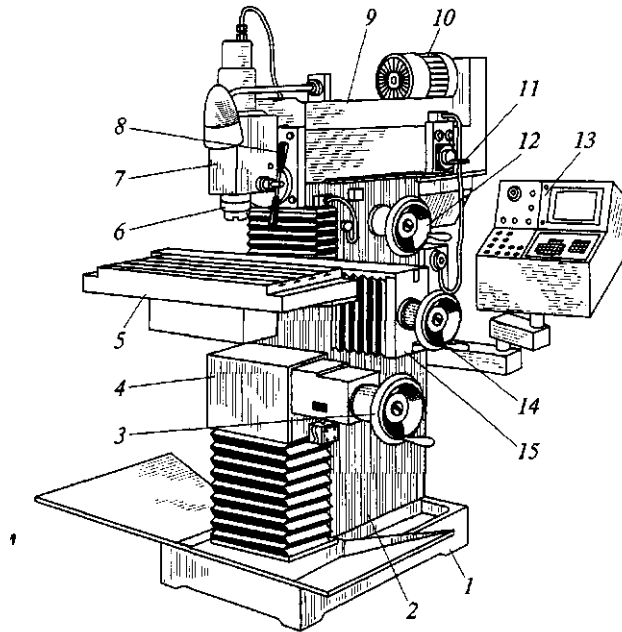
Комбинированный фрезерно-долбежный станок с ЧПУ:
